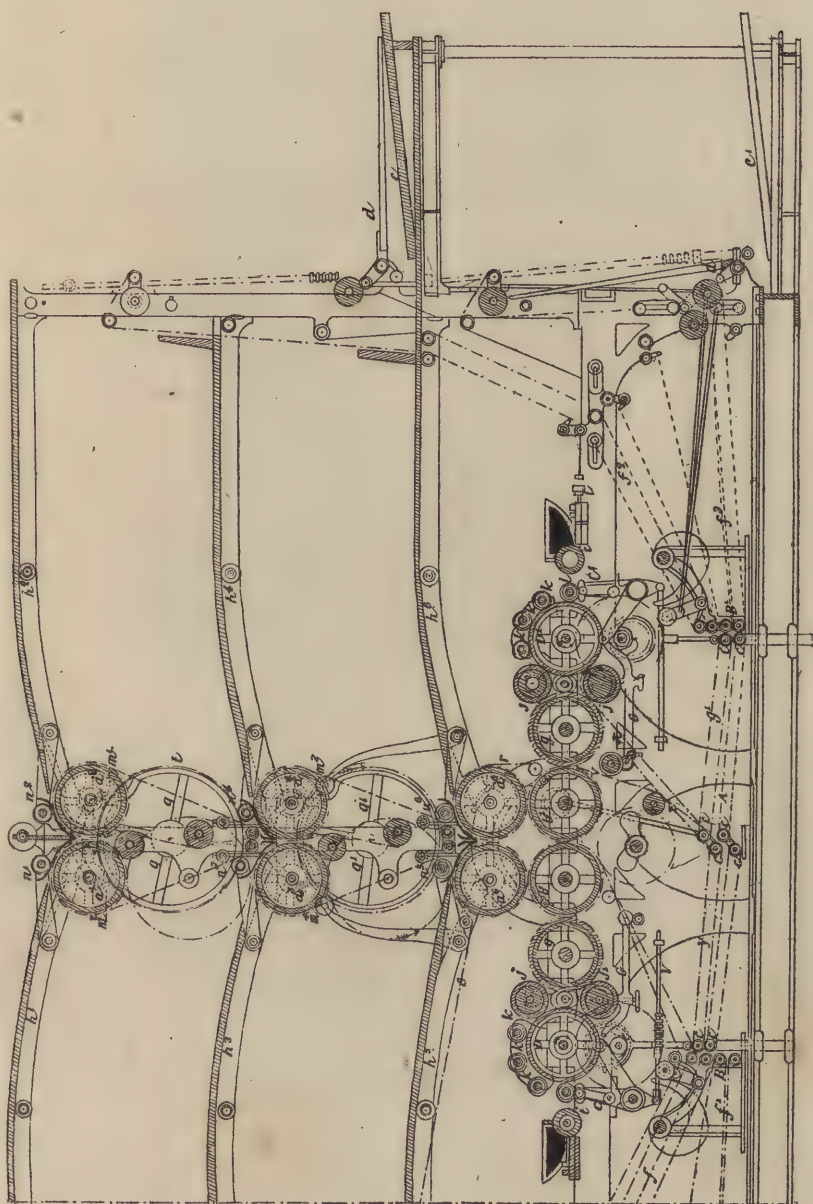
DESCRIPTION DE LA MACHINE A 6 MARGEURS, SYSTEME MARINONI.
